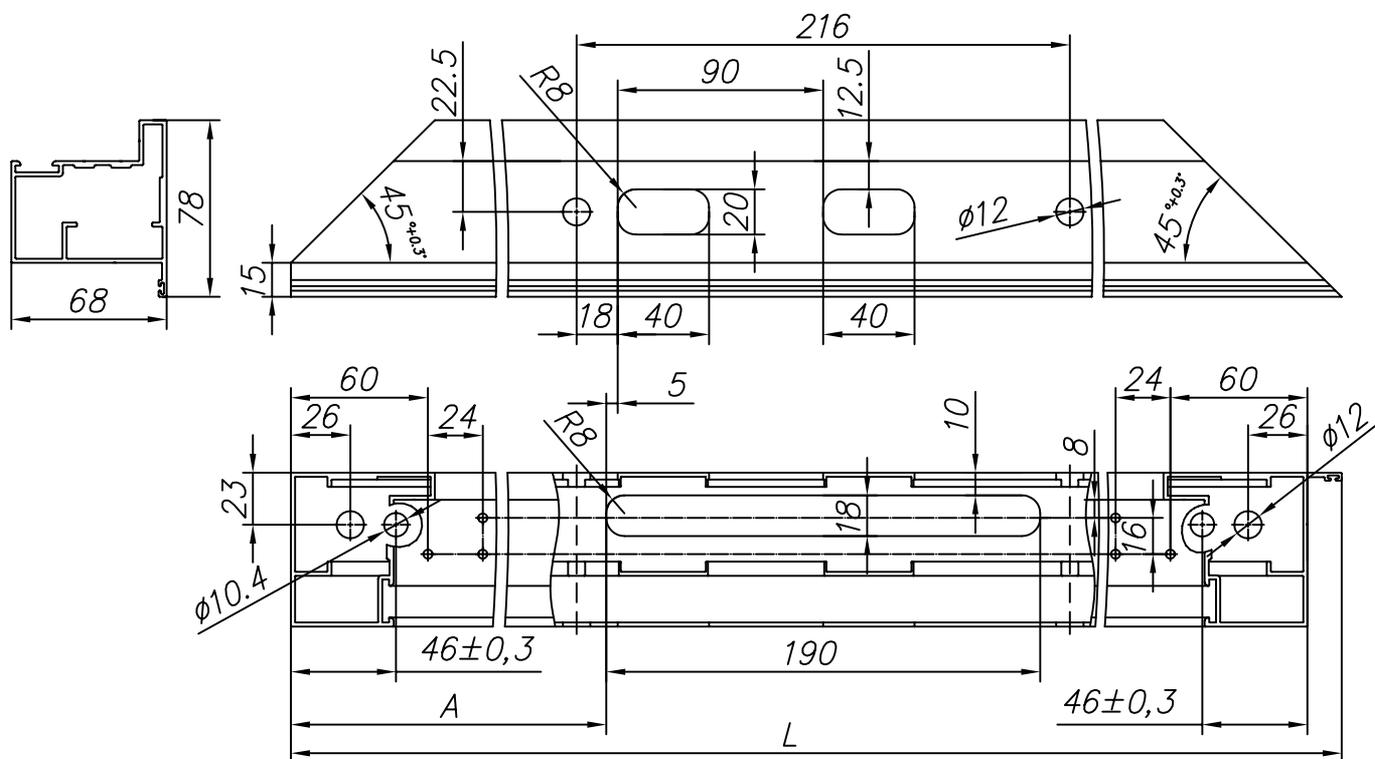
Изготовление стойки с пазом для замка из профиля FLGU.400.0108 (калитка с перекладиной, открывание наружу, вправо)
